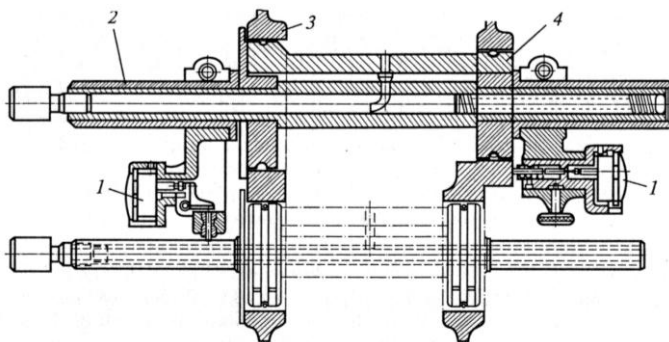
Схема проверки параллельности осей отверстий в корпусной детали:
